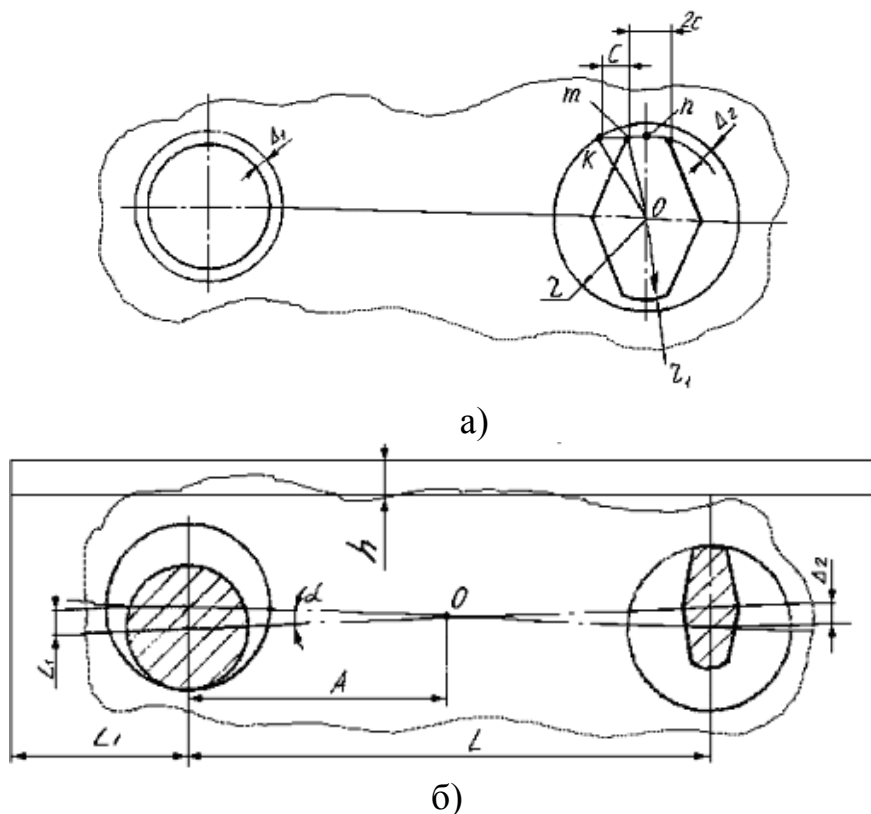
Схема для розрахунку похибки устанавлення
